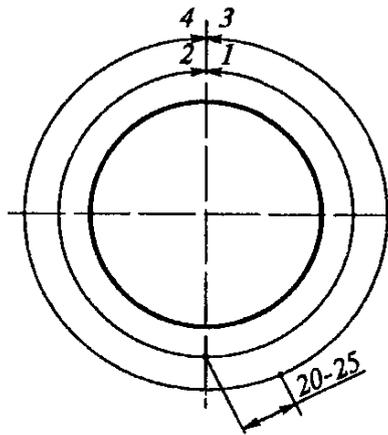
Порядок сварки неповоротного стыка труб
